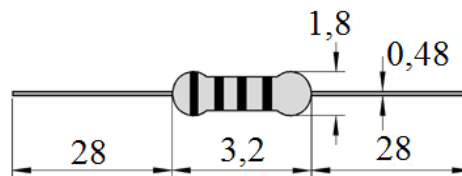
Габаритні розміри змінного резистора типу С2–23
